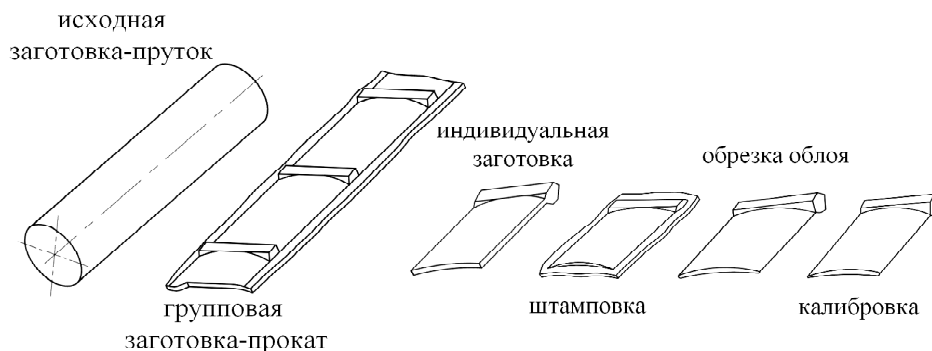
Последовательность технологических переходов точной горячей штамповки рабочих лопаток компрессора из прутка
